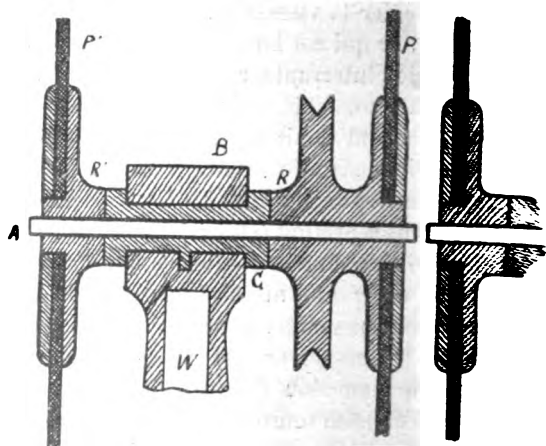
Détails de montage d'une machine de Wimshurst démontable.
